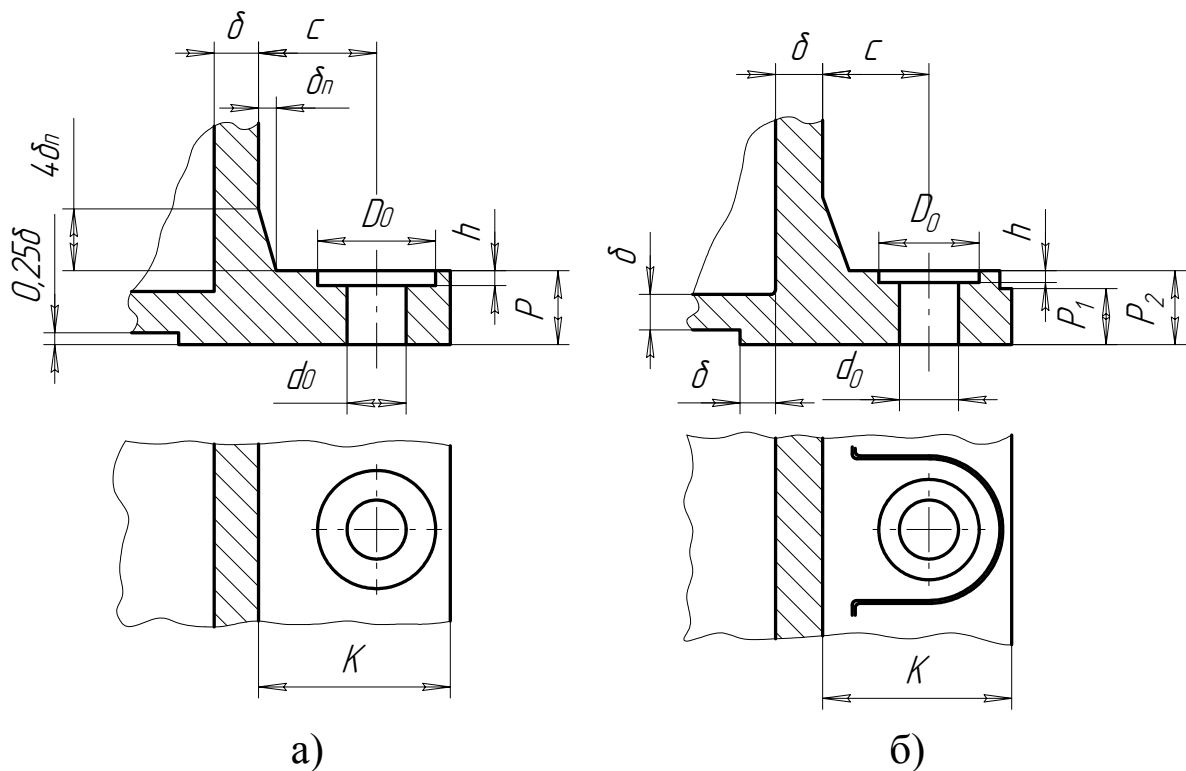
Розміри фланців підстави корпуса: а – без бобишек; б – з бобишками.
